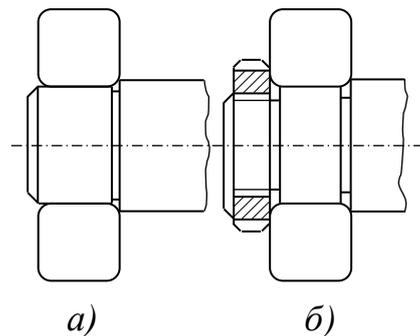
Цапфы под подшипники качения: а – цилиндрическая без крепления; б – с
